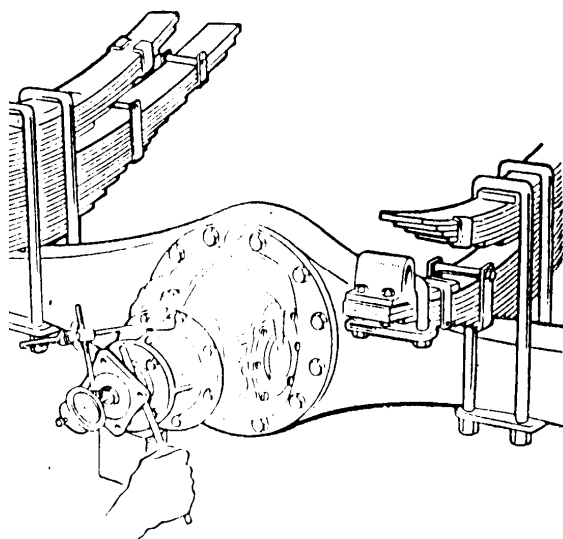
Способ проверки осевого зазора в подшипниках вала ведущей конической шестерни главной передачи автомобиля ЗИЛ-130
